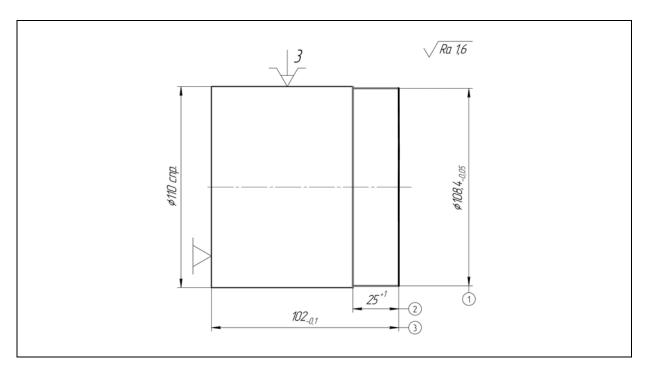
Эскиз обработки детали по предварительной токарной операции
